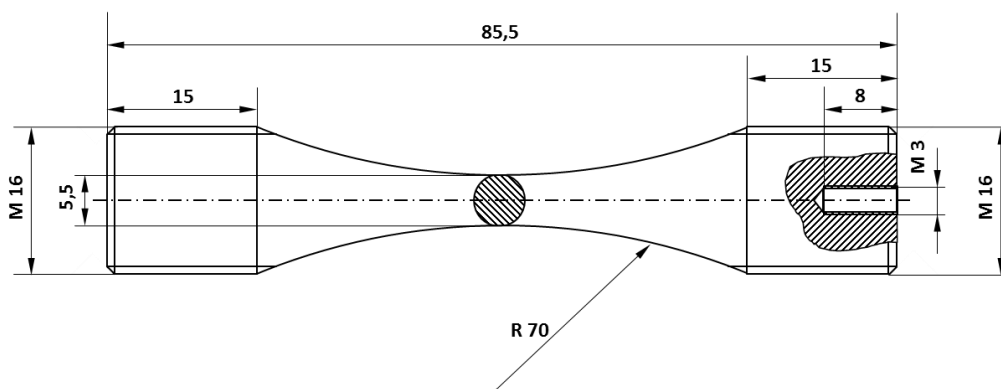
Verwendete Zugschwellprobengeometrie, für die Beschichtung wurden die M16-Gewinde maskiert
